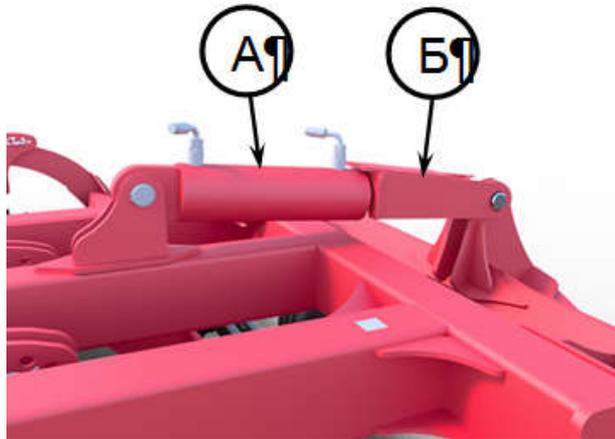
Гідроциліндр транспортного пристрою і транспортний упор в робочому положенні:
